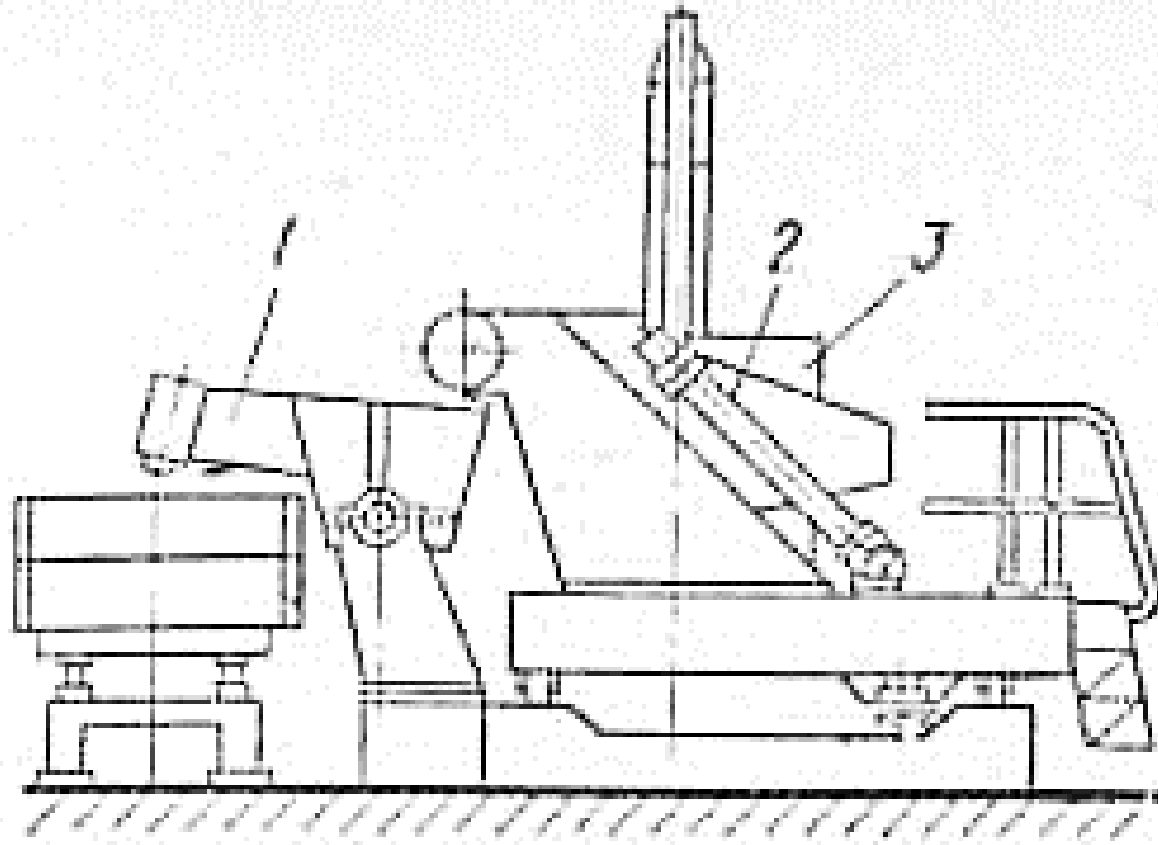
Заливочная установка автоматической линии фирмы “Кюнкель Вагнер”: 1 – жёлоб-дозатор; 2 – механизм поворота ковша; 3 – сменные ковши
